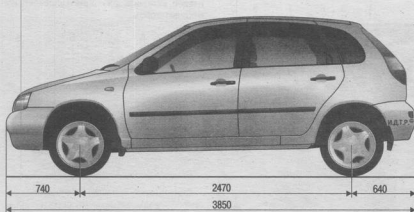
Габаритные размеры автомобиля ВАЗ-1119
